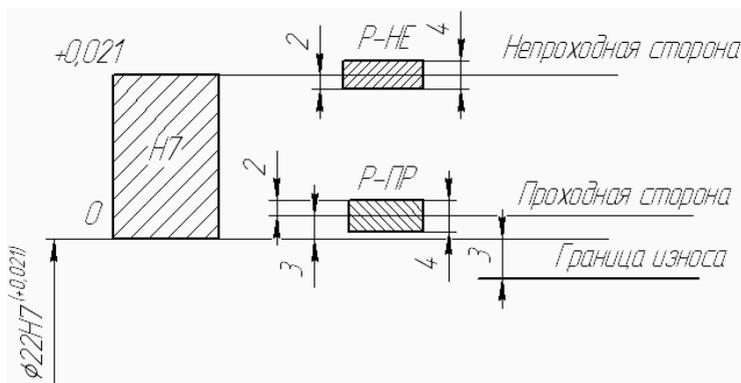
Схема полей допусков детали и гладких калибров для отверстия $\varnothing 22H7$
